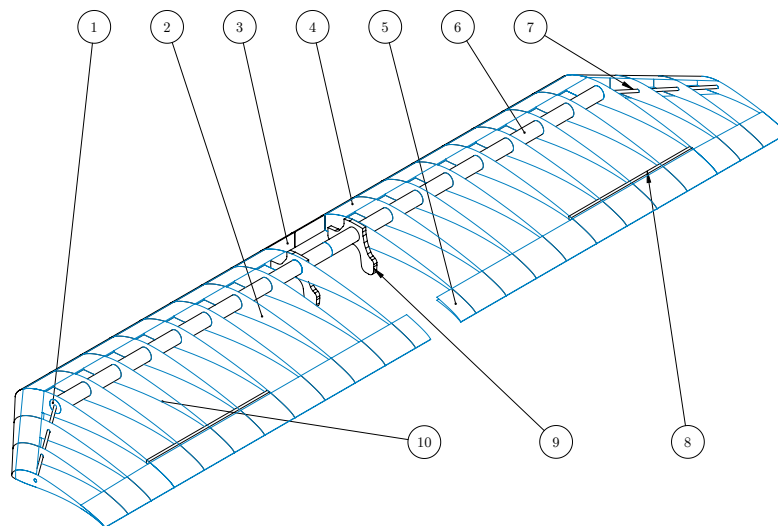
Layout estrutural e detalhamento da asa projetada pela equipe Draco Volans Aerodesign
